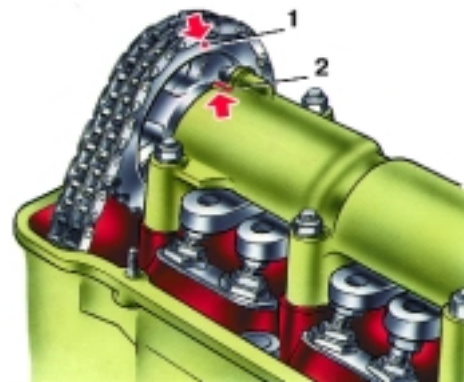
Установка поршня 4-го цилиндра двигателя мод. 2106–70 в в.м.т. в конце такта сжатия: 1 — установочная метка на звездочке распределительного вала; 2 — установочный прилив на корпусе подшипников распределительного вала
